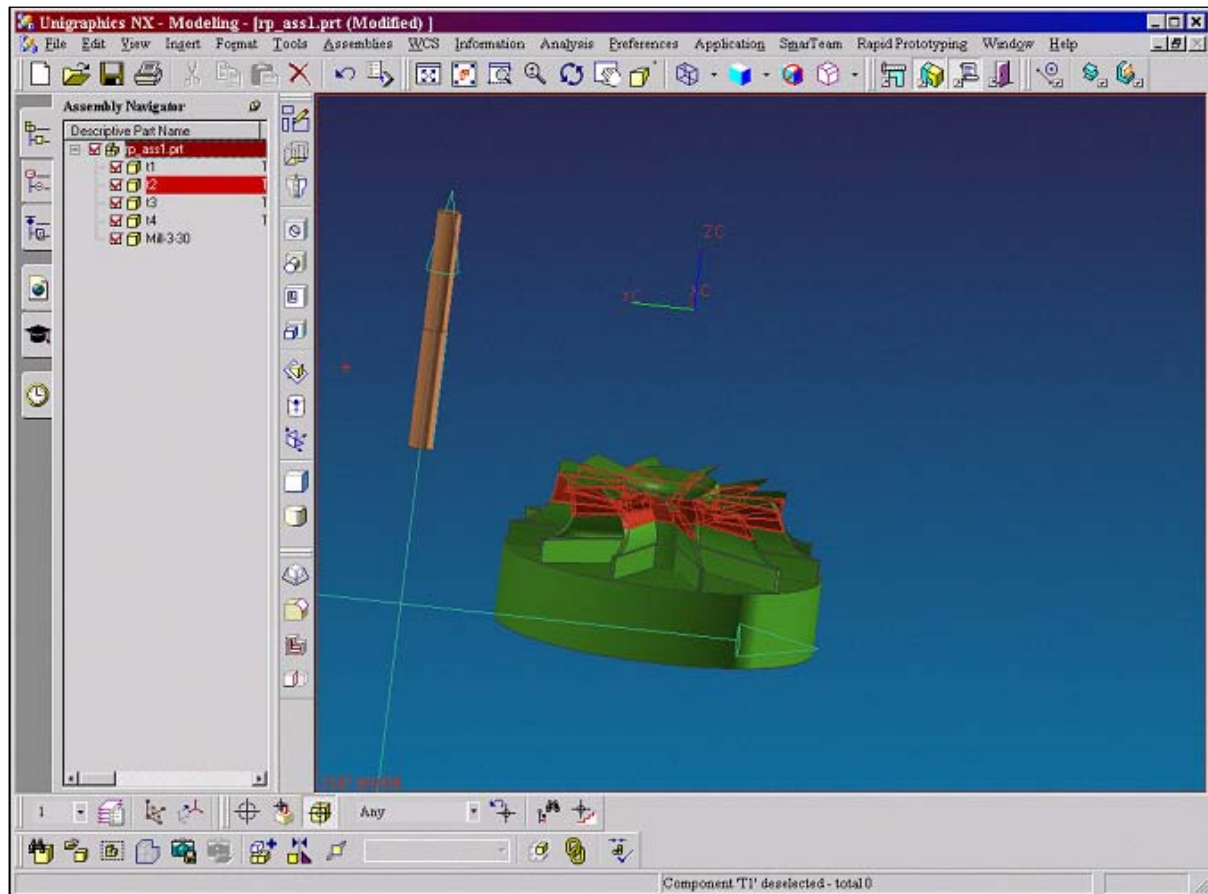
Baugruppe mit Bauteil und Fräser [3]
